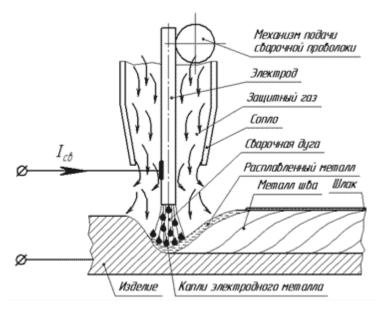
Схема сварки в защитных газах
